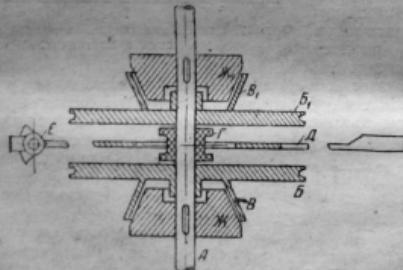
Станок Гаузер для сверления гнезда ремонтуара:
